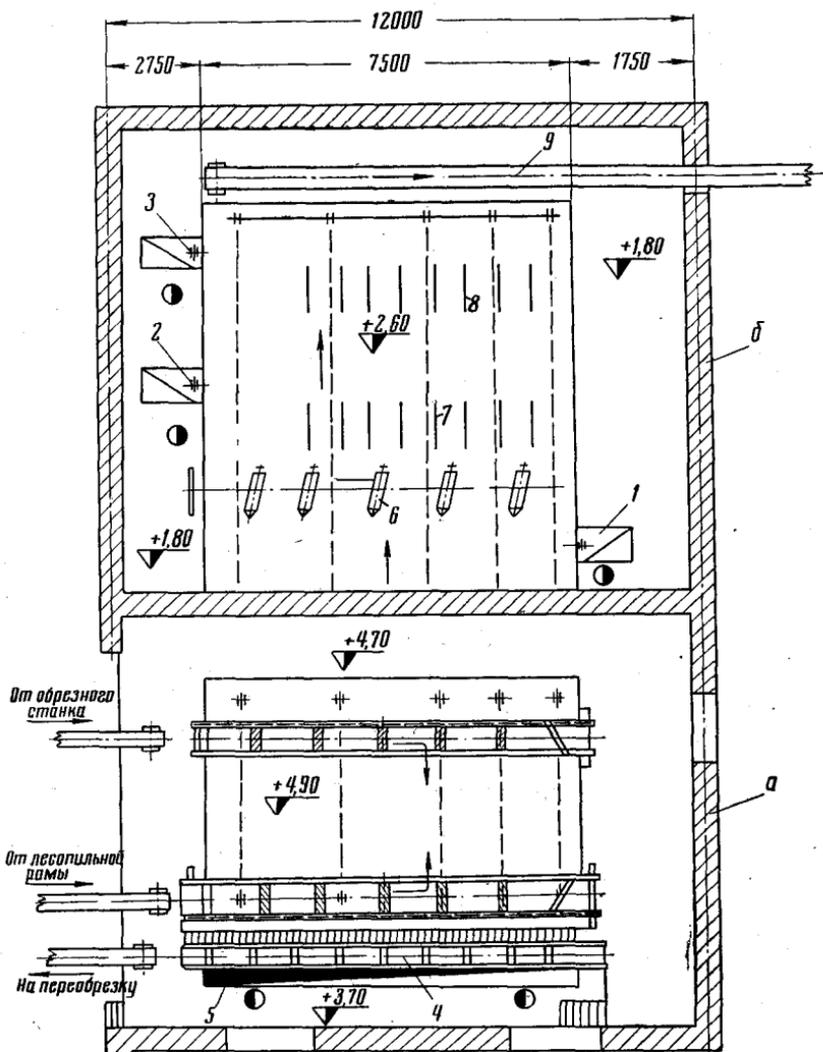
Расположение браковочно-разметочного устройства и торцовочных станков на транспортере
